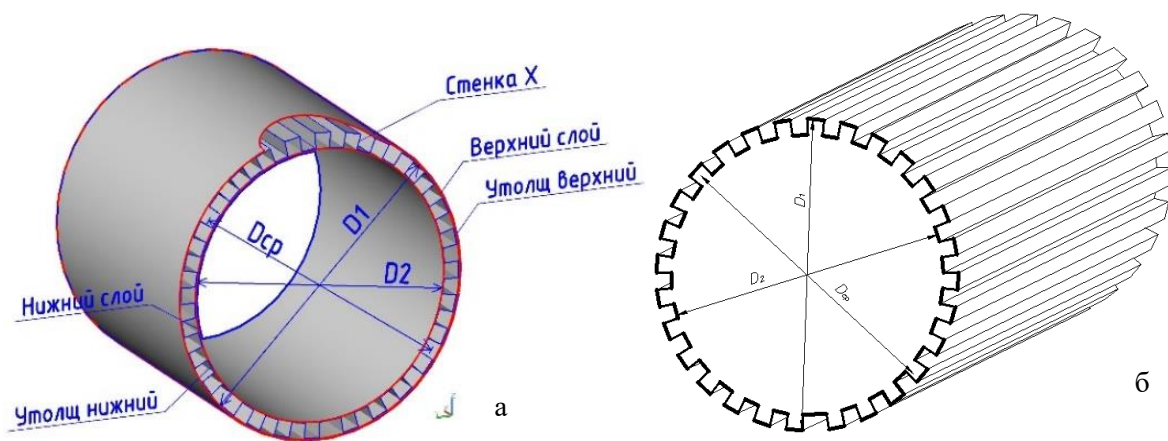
Фрагмент трехслойной цилиндрической оболочки (а), с заполнителем в виде гофра (б)
